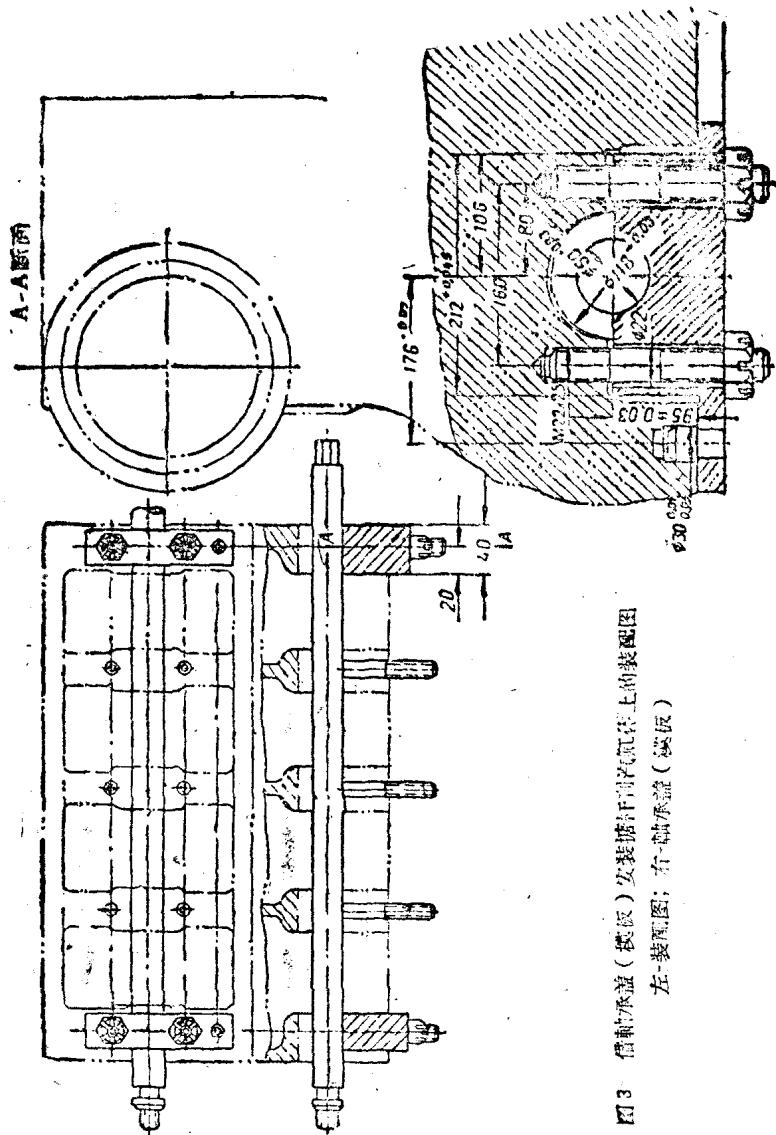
带轴承底盖(底板)安装于气流气筒上的装配图
